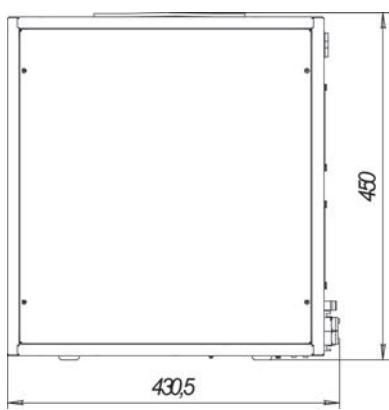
Габаритный чертеж НЭВ 75-2000
